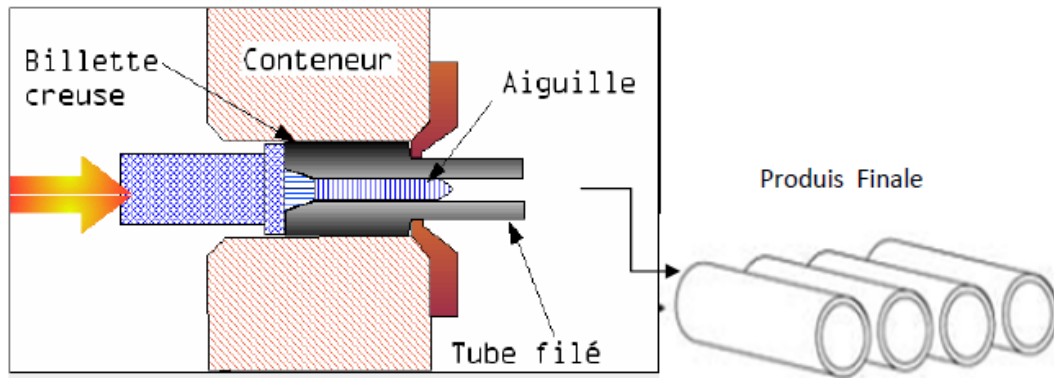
Fabrication d'un pipeline sans soudure « Schéma du filage sur aiguille permettant D'obtenir un tube sans soudure » [30].
